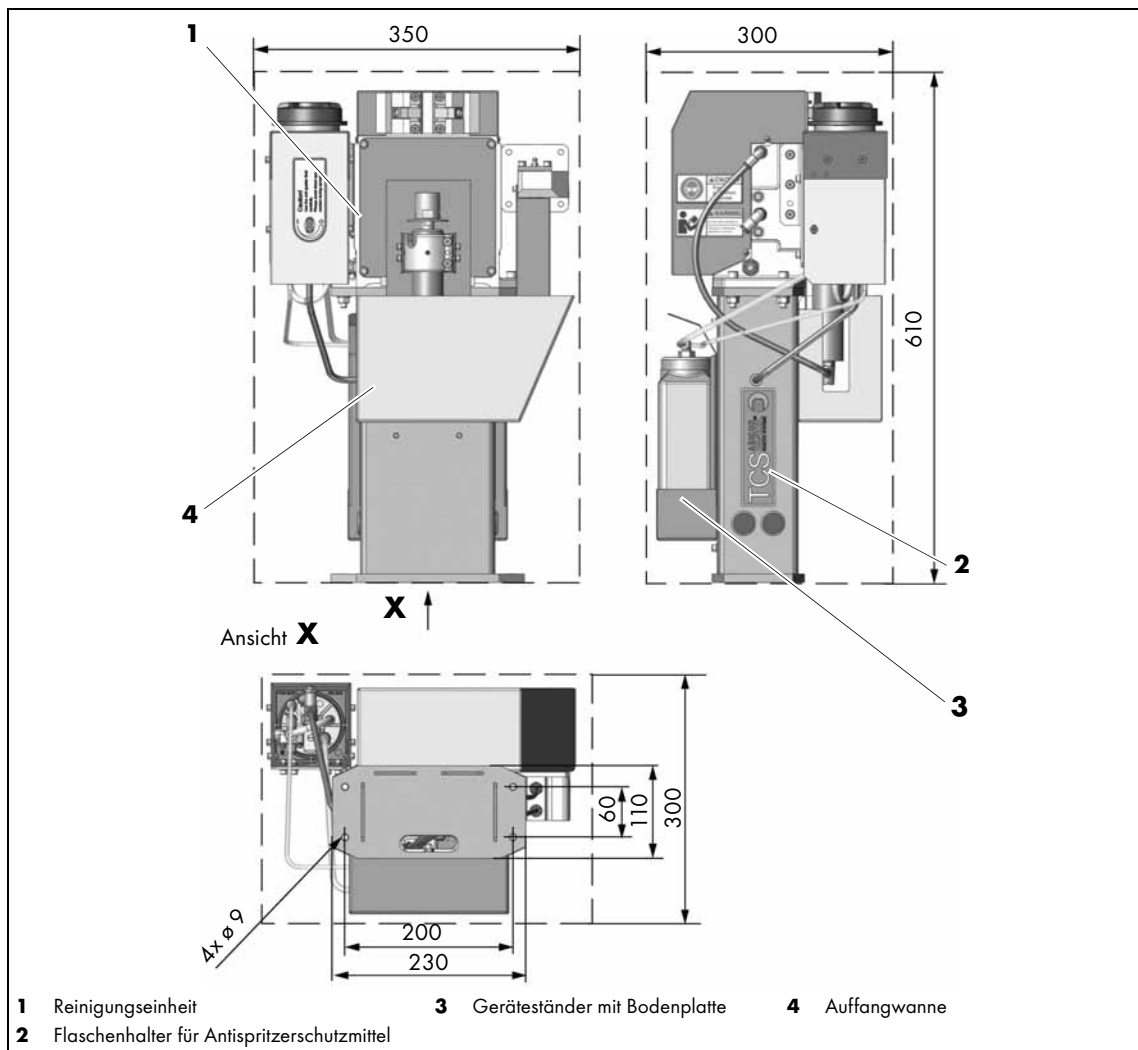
Technische Daten - Ausführung mit langem Geräteständer
